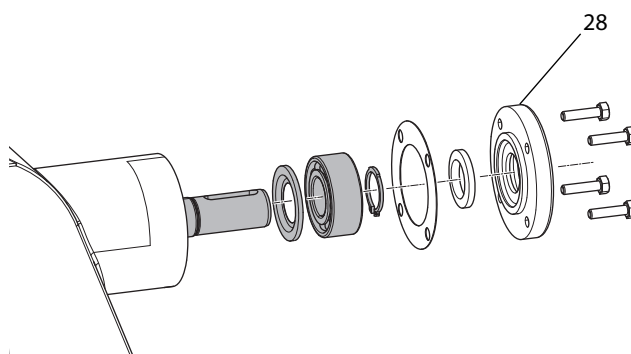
Forma constructiva L1, eje de la bomba, lado del motor
